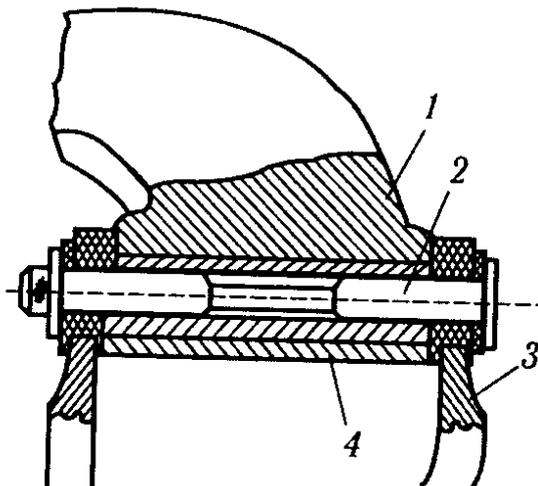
Схема восстановления кронштейна: 1 – кронштейн для валика подвески башмака; 2 – валик подвески; 3 – подвеска башмака; 4 – втулка волокнистая; 5 – втулка резиновая
